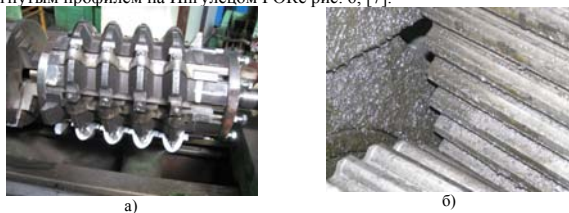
Червячная фреза для обработки зубчатого колеса с профилем Новикова (а) и изготовленная зубчатая передача (б).
